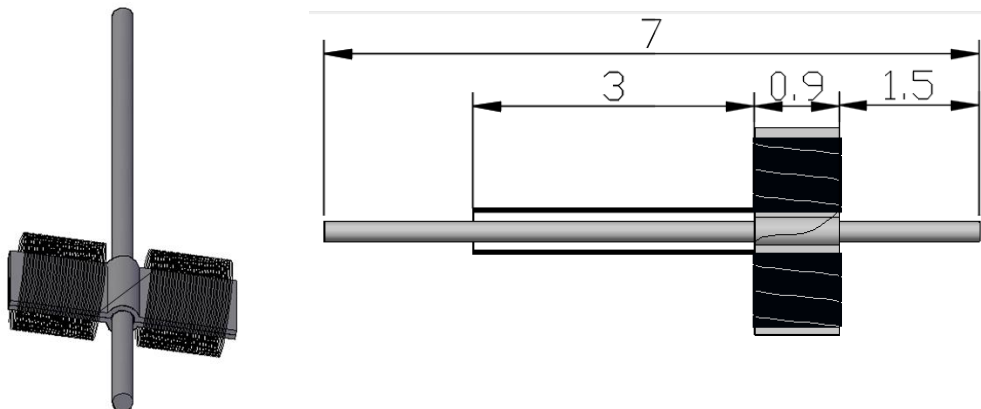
Vista en perspectiva y vista superior de la armadura montada en el eje.
